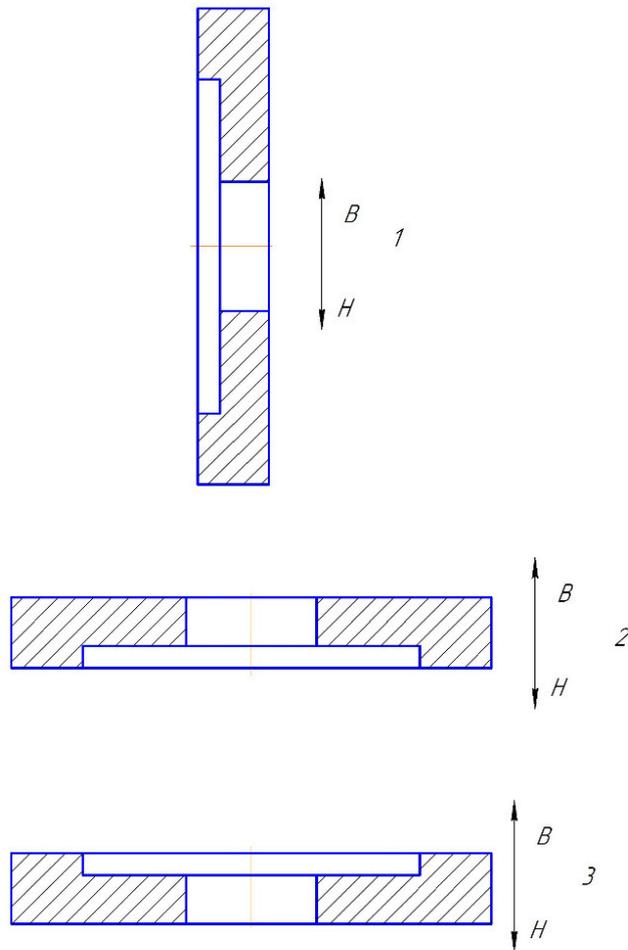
Варианты расположения отливки в форме в период заливки и затвердевания
